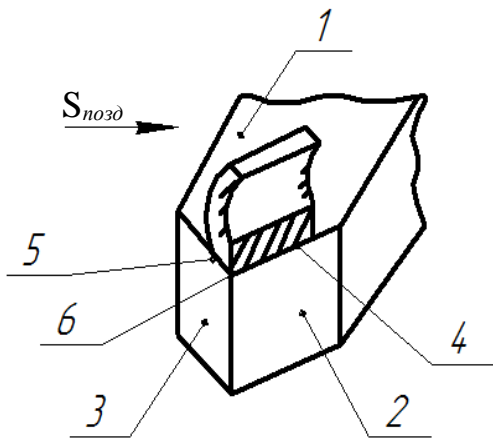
Поверхні й інші елементи різальної частини інструмента
